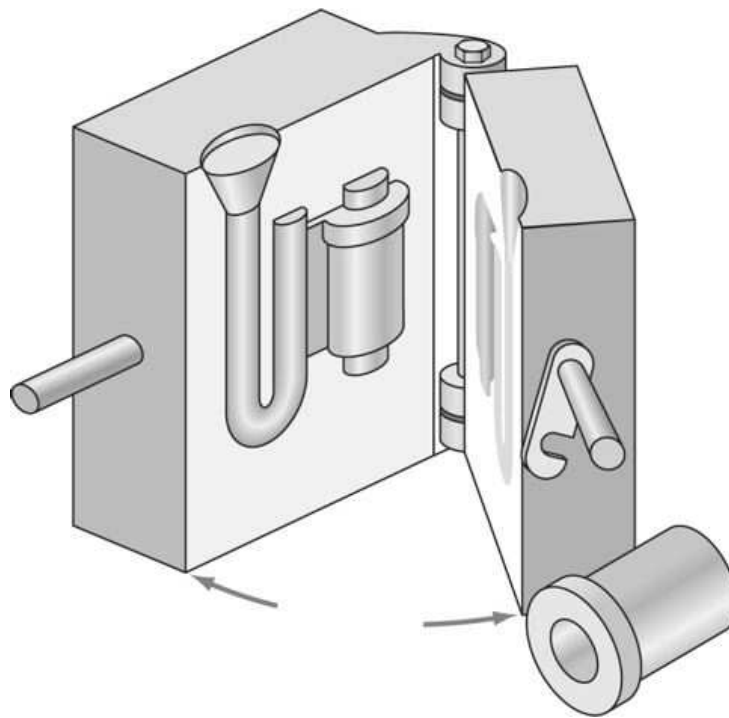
Molde permanente o coquilla para fundición. En la mitad izquierda del molde se muestra la colada solidificada con la entrada y el núcleo de metal. El producto acabado se muestra delante del molde (William, 1998).
